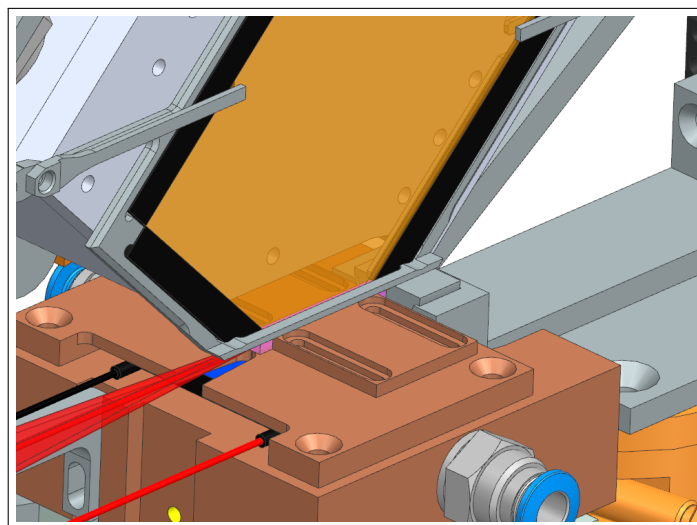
Zoom sur la vue de 3/4 de la nouvelle mécanique "version 2"
